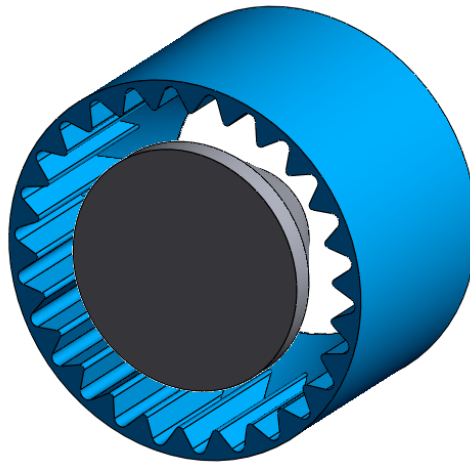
Imagen del CAD del tercer tipo de soporte de la pieza 6 en el que se puede observar en color azul la parte externa del soporte y en color gris la parte interna del mismo.
